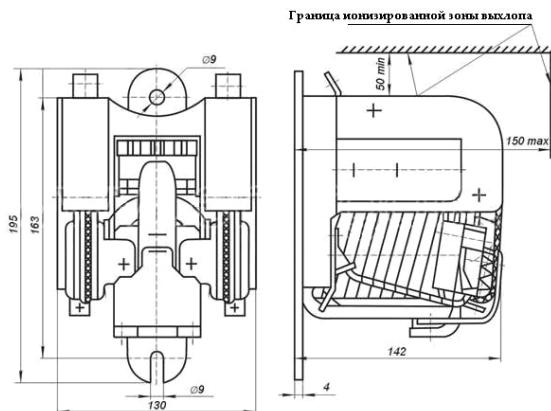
Габаритные, установочные размеры КПД-121 У2
